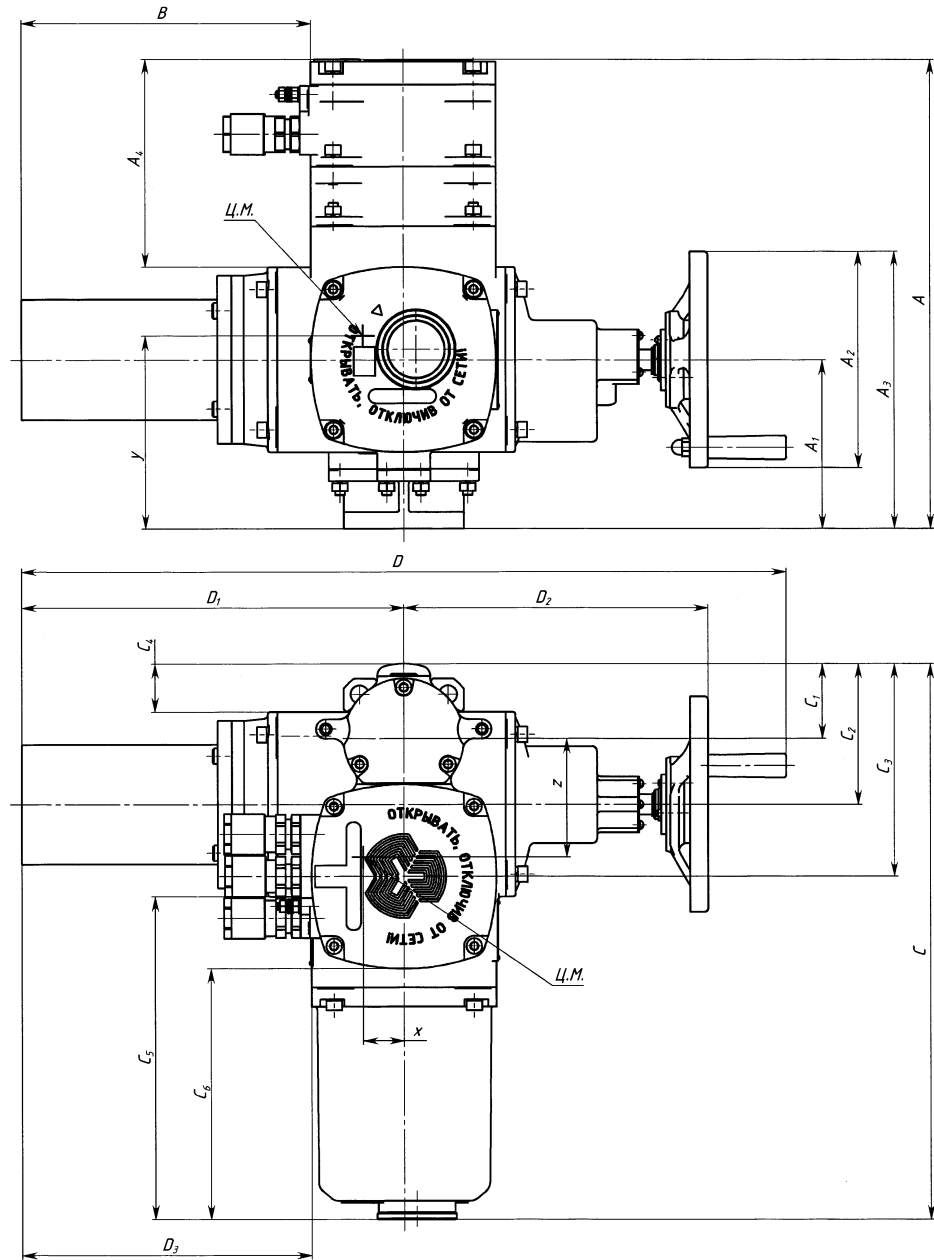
а – Габаритные размеры привода конструктивной схемы 40
